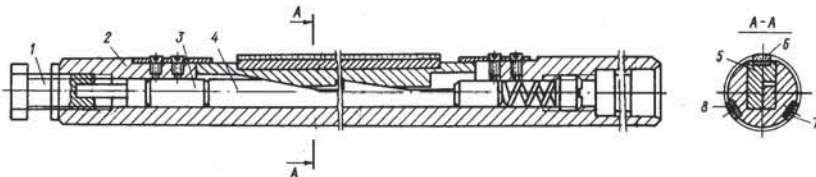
Хонинговальная головка для обработки отверстий диаметром 10...30 мм
